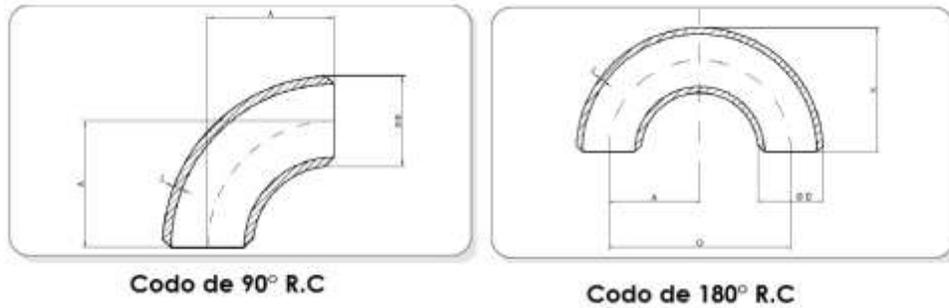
Tipos de codos de radio largo de 90° y 180°. Fuente: Catalogo Tubos y accesorios en acero al carbono soldado y sin soldadura Normas EN (DIN) y ASTM. Tubasol S.A
